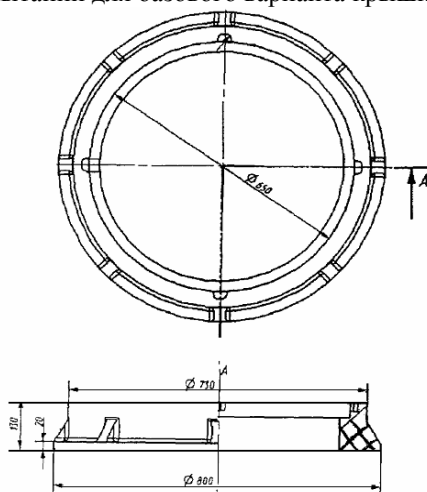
Конструкция и основные размеры базового варианта крышки и корпуса люка
